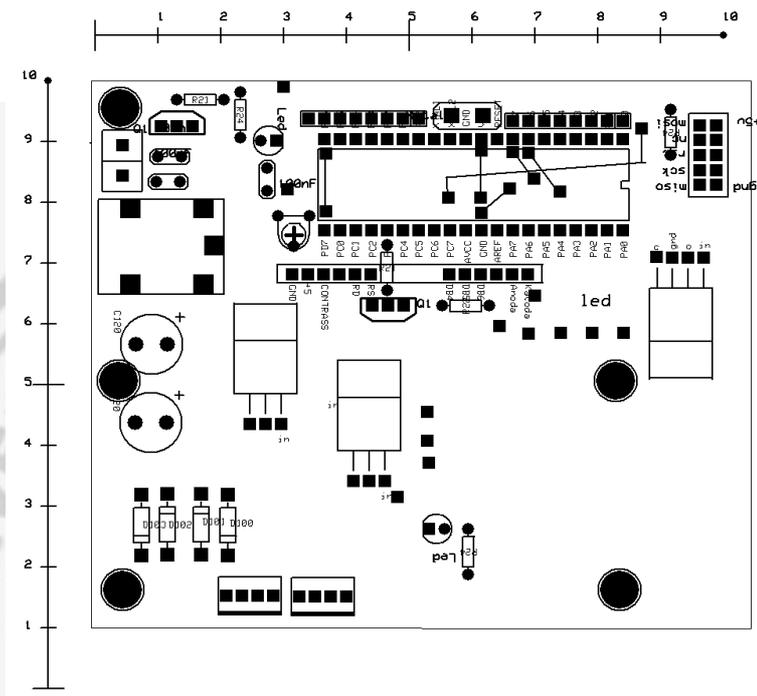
Layout PCB Mikrokontroler ATmega8535
